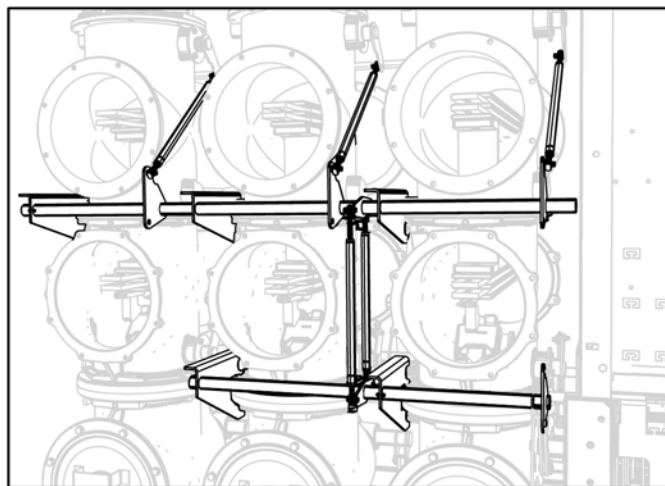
Монтажное положение кинематических компонентов на верхнем и нижнем корпусах сборных шин
